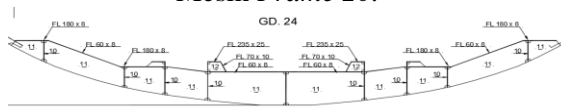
Konstruksi Pondasi Mesin Tampak Atas.
